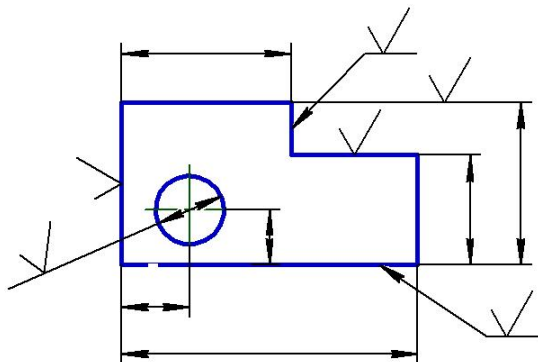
Расположение знака обозначения шероховатости на изображении
